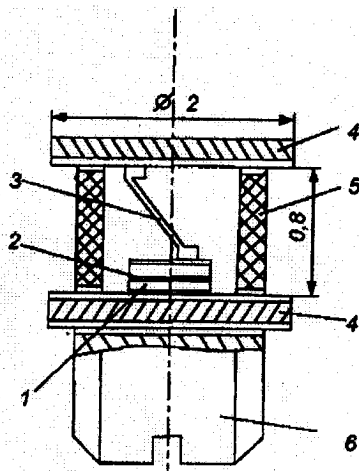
Пристрій одного із типових корпусів ЛПД для частот до 18ГГц (всі з'єднані поверхні металізовані під пайку): 1 – основа для кріплення структури; 2 – напівпровідникова структура; 3 – з'єднувач; 4 – коваровий диск; 5 – керамічний циліндр; 6 – мідний штифт з різьбою
